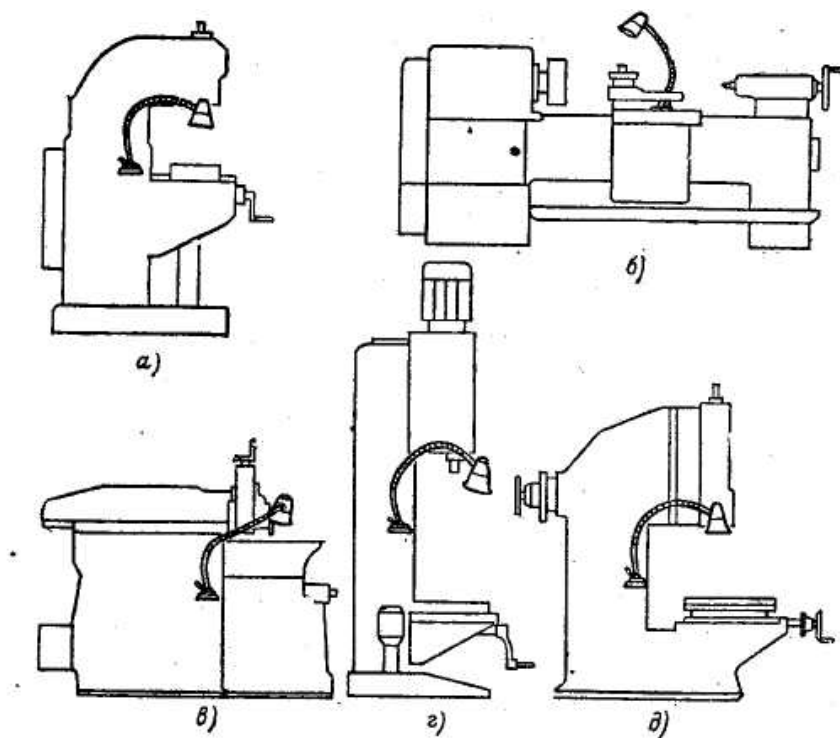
Схеми установки світильників місцевого освітлення на металообробних верстатах: а — фрезерно-центрувальний; б — токарний; в — розточний; г — свердлильний; д — шпон очно-фрезерний.
